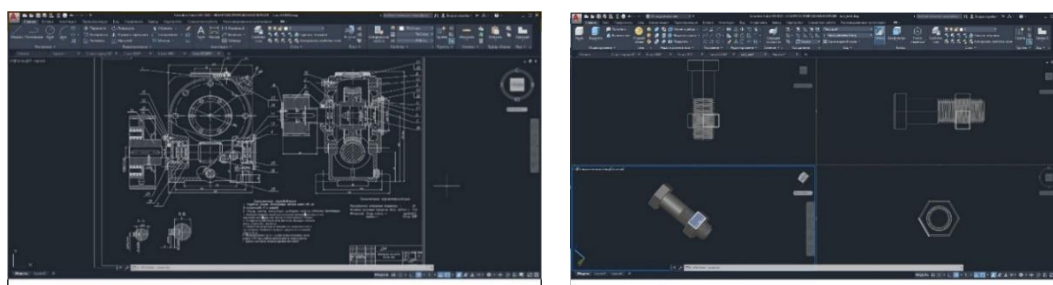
Изображение чертежа червячного редуктора и 3D модели детали
